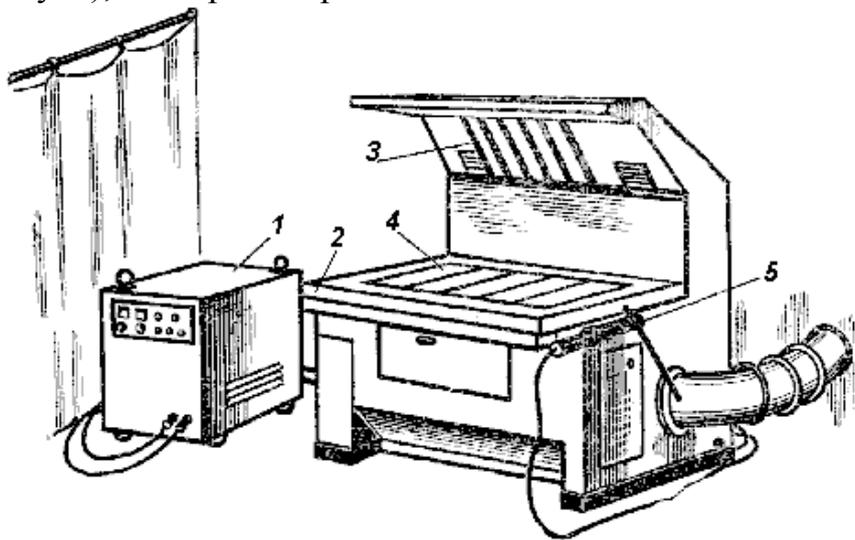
Общий вид стационарного поста для ручной дуговой сварки
